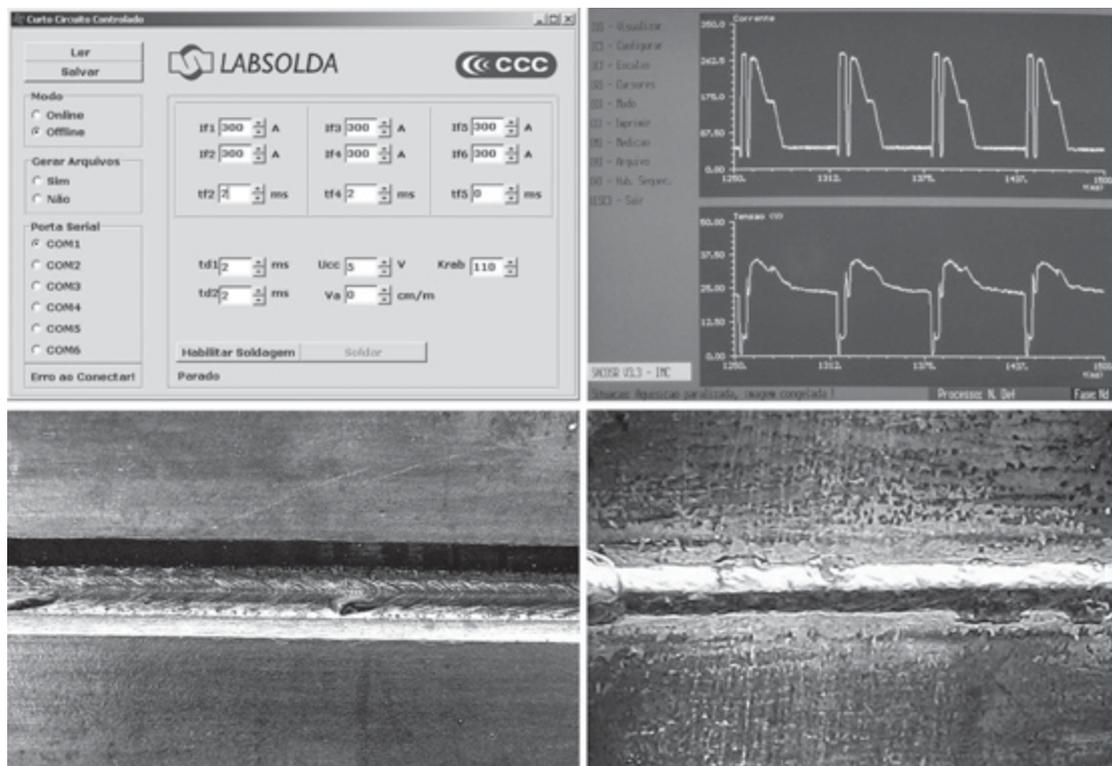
Soldagem de raiz feita com o processo CCC (Interface da plataforma, aquisição de sinais e cordão obtido)
